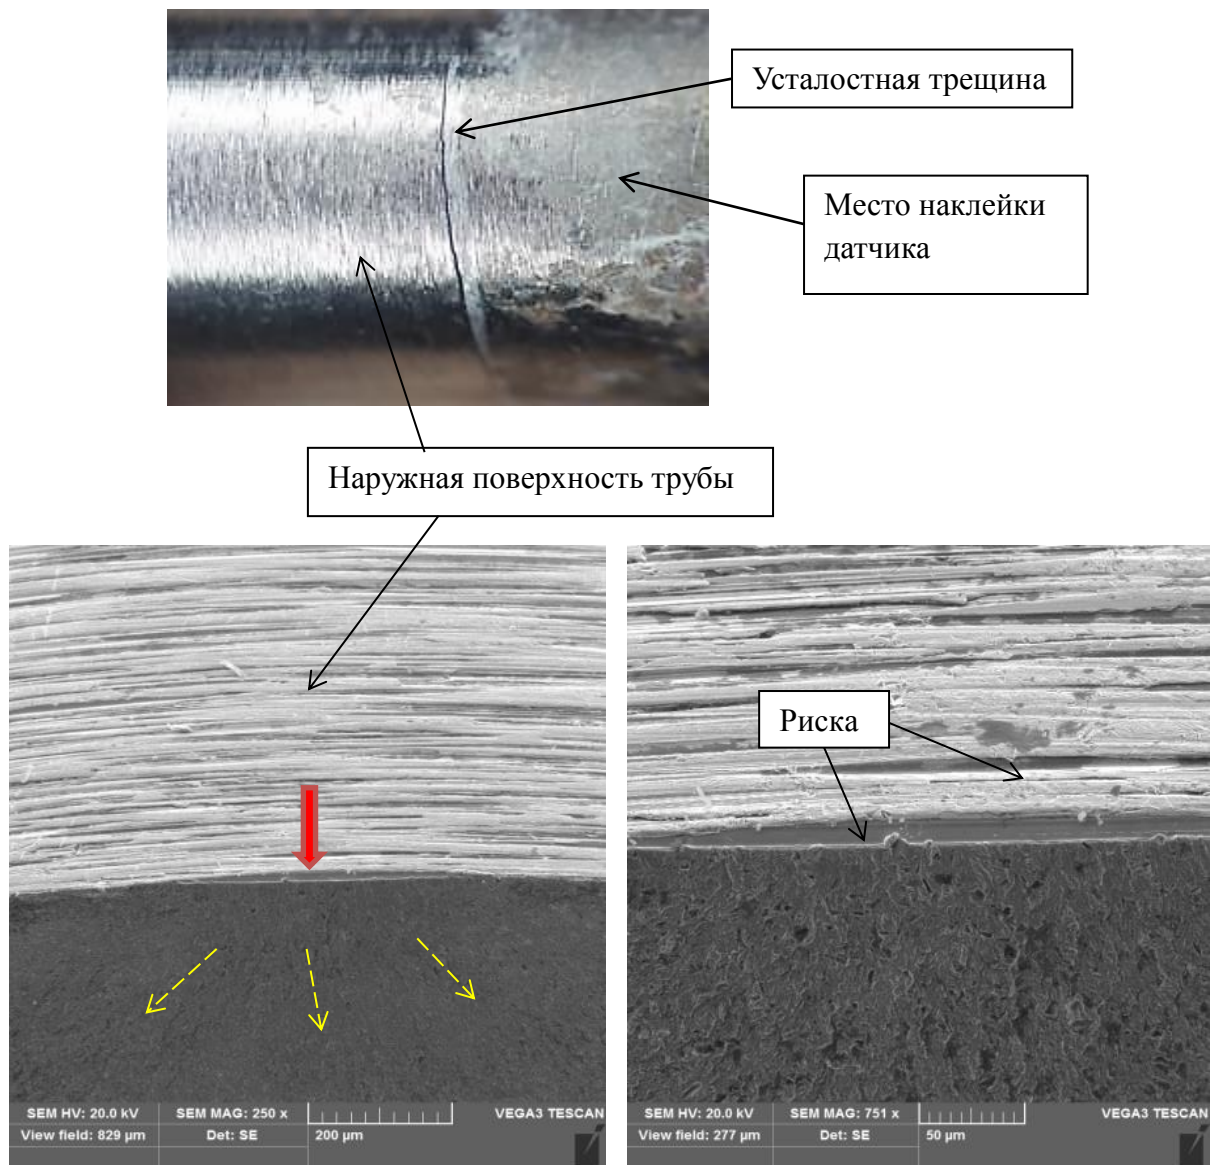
Вид усталостной трещины (и вид излома по ней), развивающейся от кольцевой риски на наружной поверхности образца трубы 1-1 (шлифованный, группы А). Усталостные испытания проведены в условиях, исключающих возникновения ФК.
